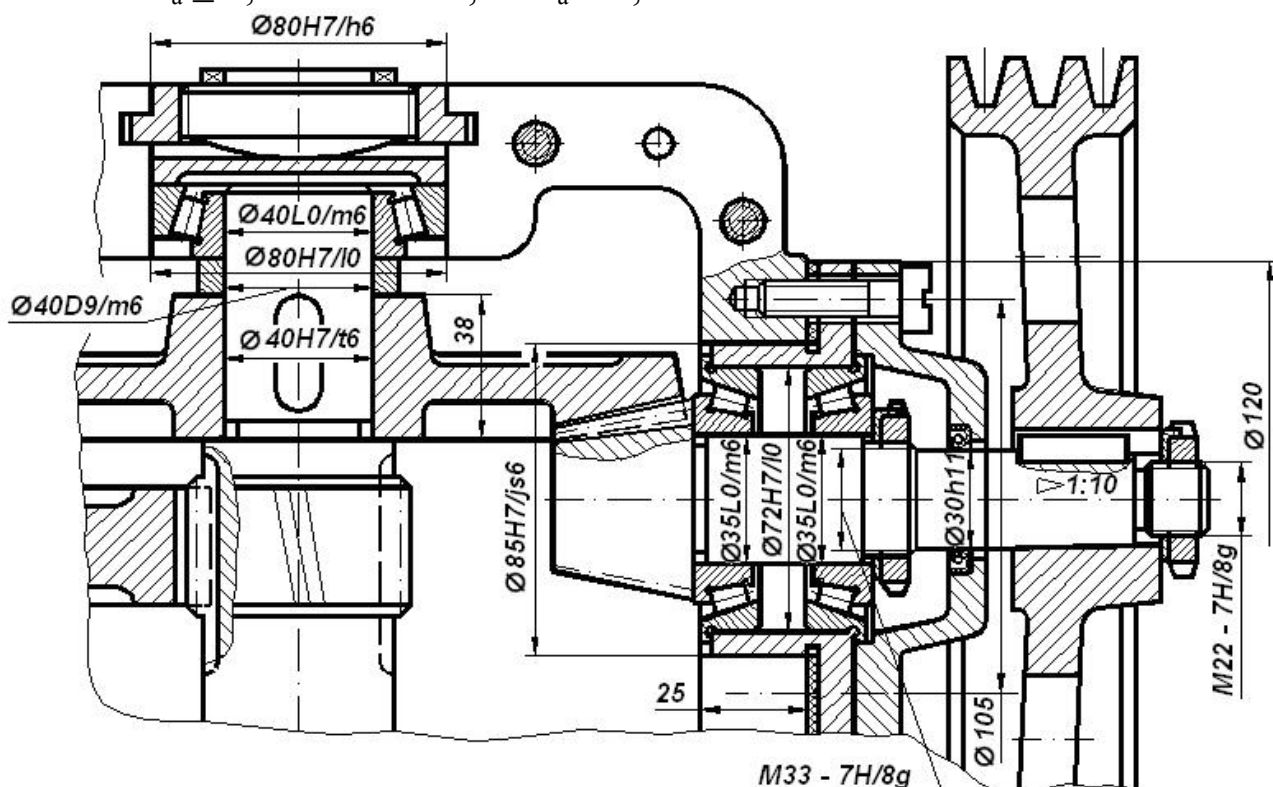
Складання одиниця конічно-циліндричного редуктора.
